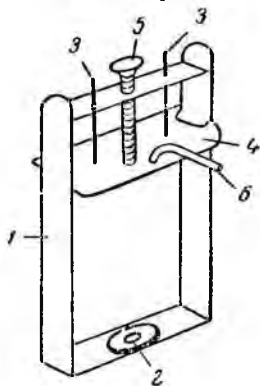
Зажим для испытания противогазовых коробок в воде: 1 — рамка; 2 — резиновый круг; 3 — направляющий стержень; 4 — металлическая пластинка; 5 — винт; 6 — трубка.
